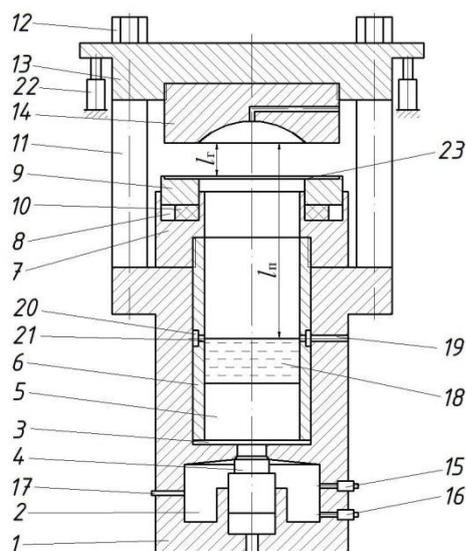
Схема импульсной машины для гидродинамической штамповки
